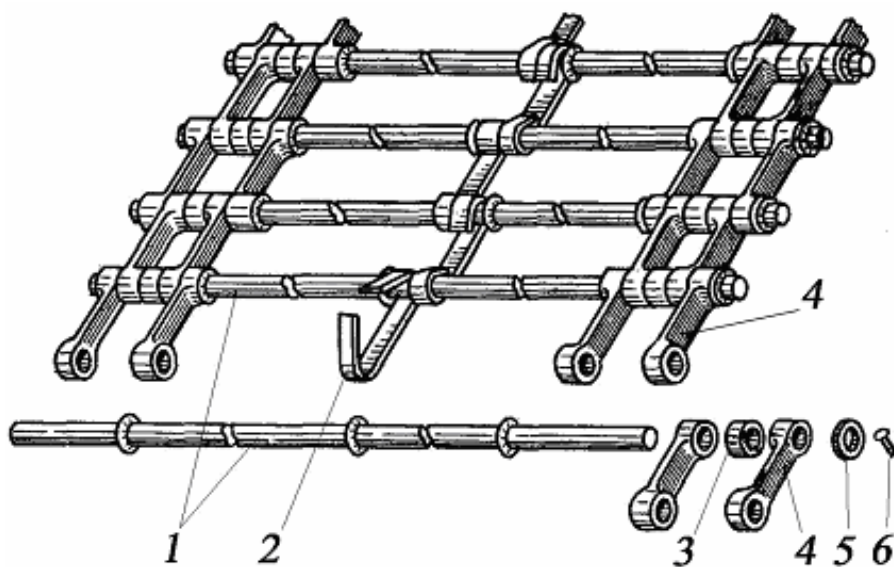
Полотно швидкісного елеватора: 1 - прутки; 2 - скоба; 3 - ролик; 4 - ланка; 5 - шайба; 6 - заклепка
